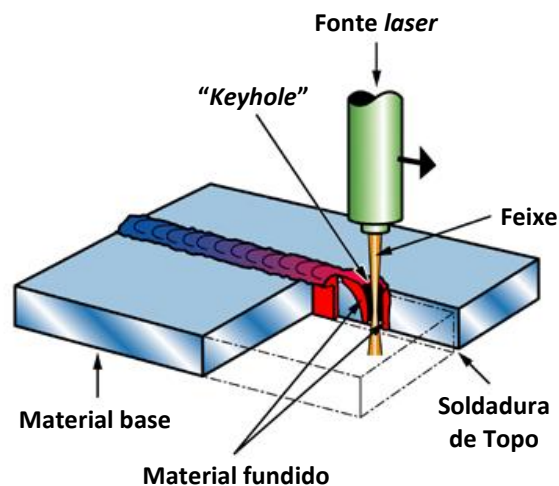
Representação Simplificada do Processo de Soldadura Laser (adaptado de [58]).
